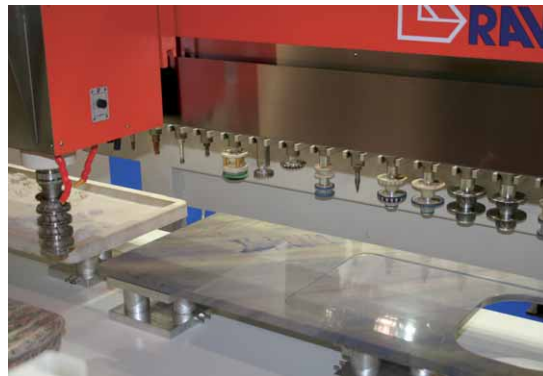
Mehrstufige Werkzeuge im Magazin eines Ravelli-CNC-Bearbeitungszentrums. In der Werkzeugspindel befindet sich ein vierstufiges Fräs- und Schleifwerkzeug.
